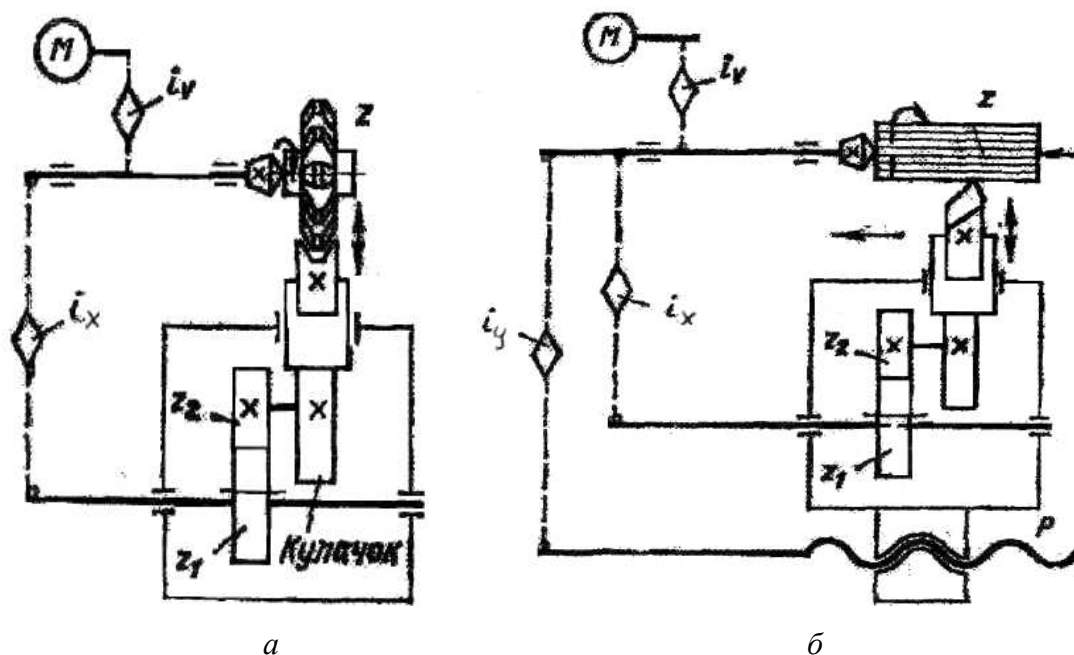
Типовые структурные схемы токарно-затыловочных станков:
